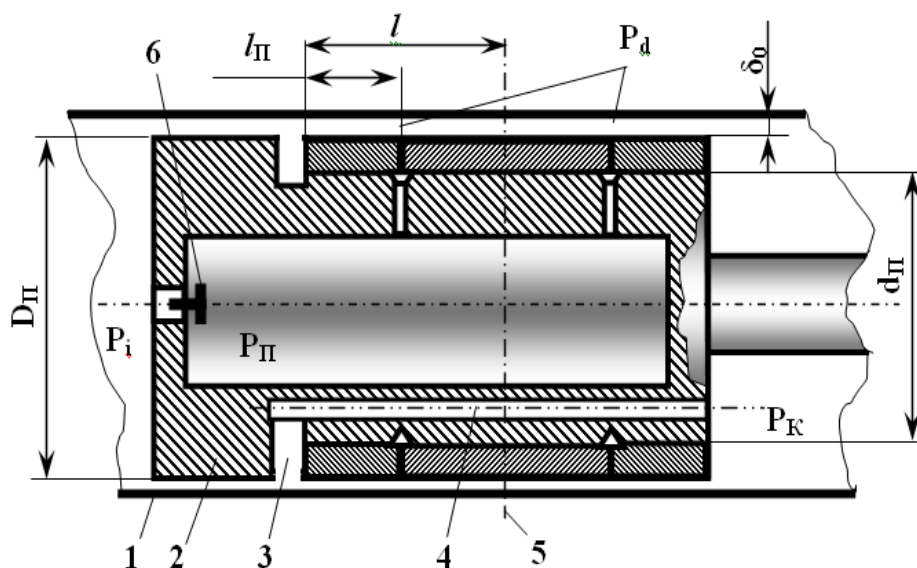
Схема цилиндрической пары компрессора с щелевыми питателями газового подвеса поршня, образованными при контакте шероховатых торцов трех втулок:
